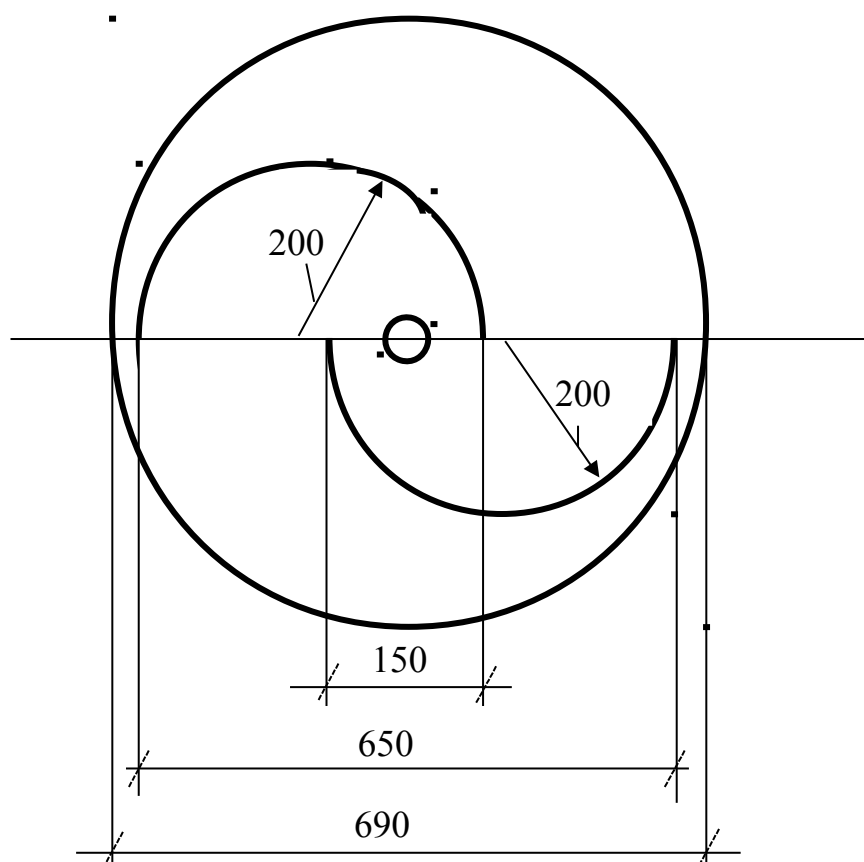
Конструкция лопастей ветродвигателя роторного типа
